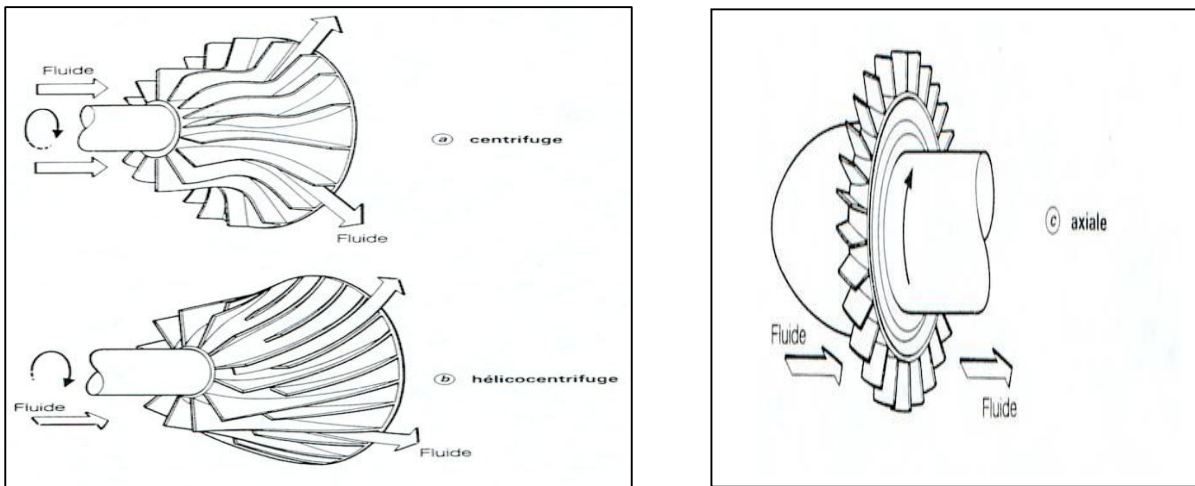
Roues mobiles de machines centrifuge, hélico centrifuge et axiale.
